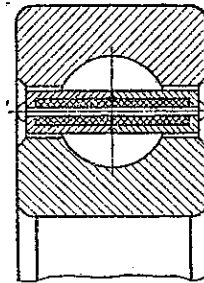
Шарикоподшипник, в сепаратор которого запрессована твердая смазка
